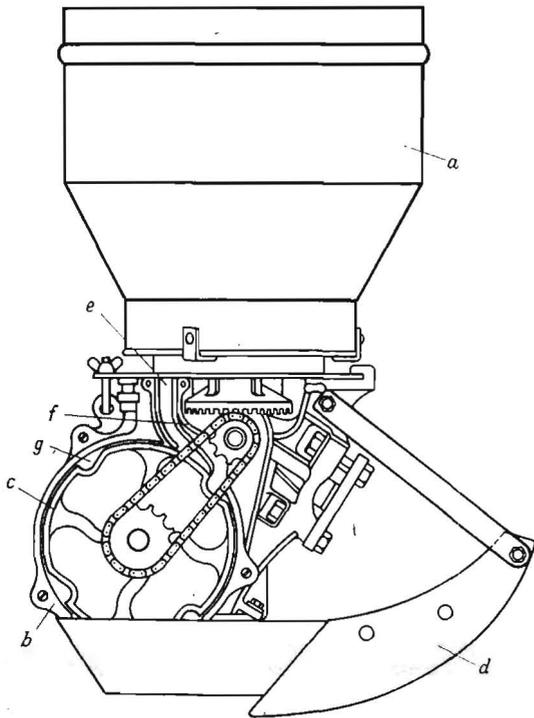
Dosier- und Austragvorrichtung für Dibbelmaschine
